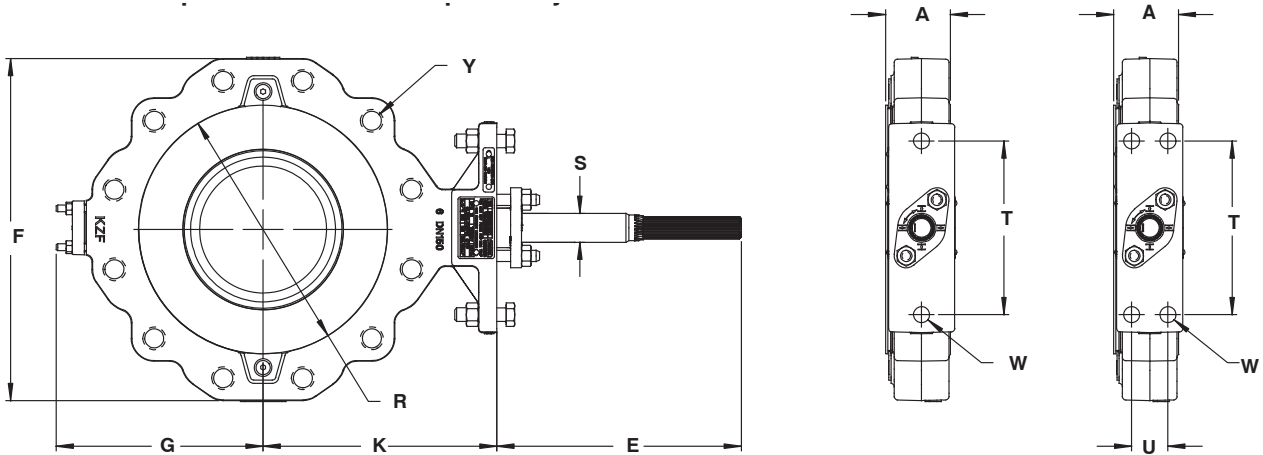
Размеры затвора 8580 (однофланцевый корпус с проушинами)
